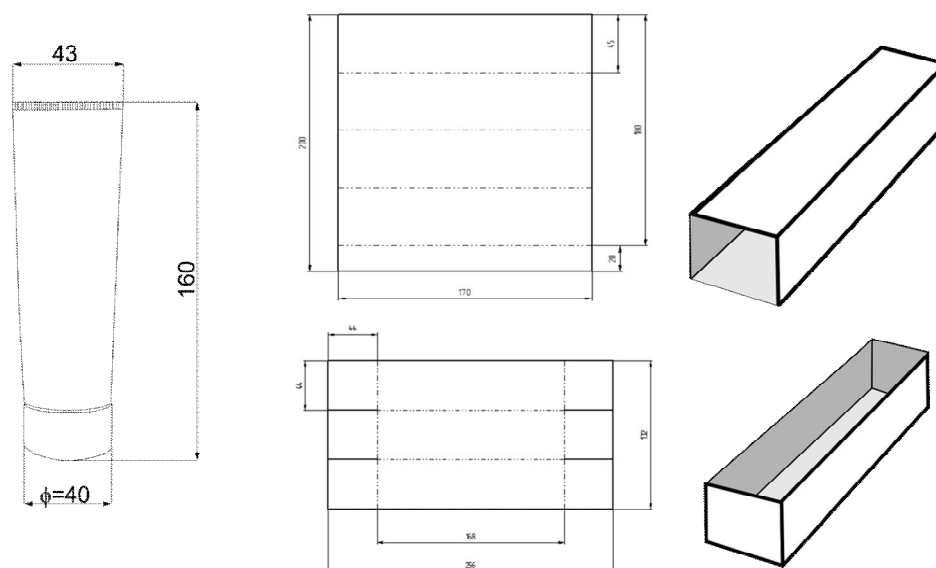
Конструкция первичной и вторичной упаковки для зубной пасты
